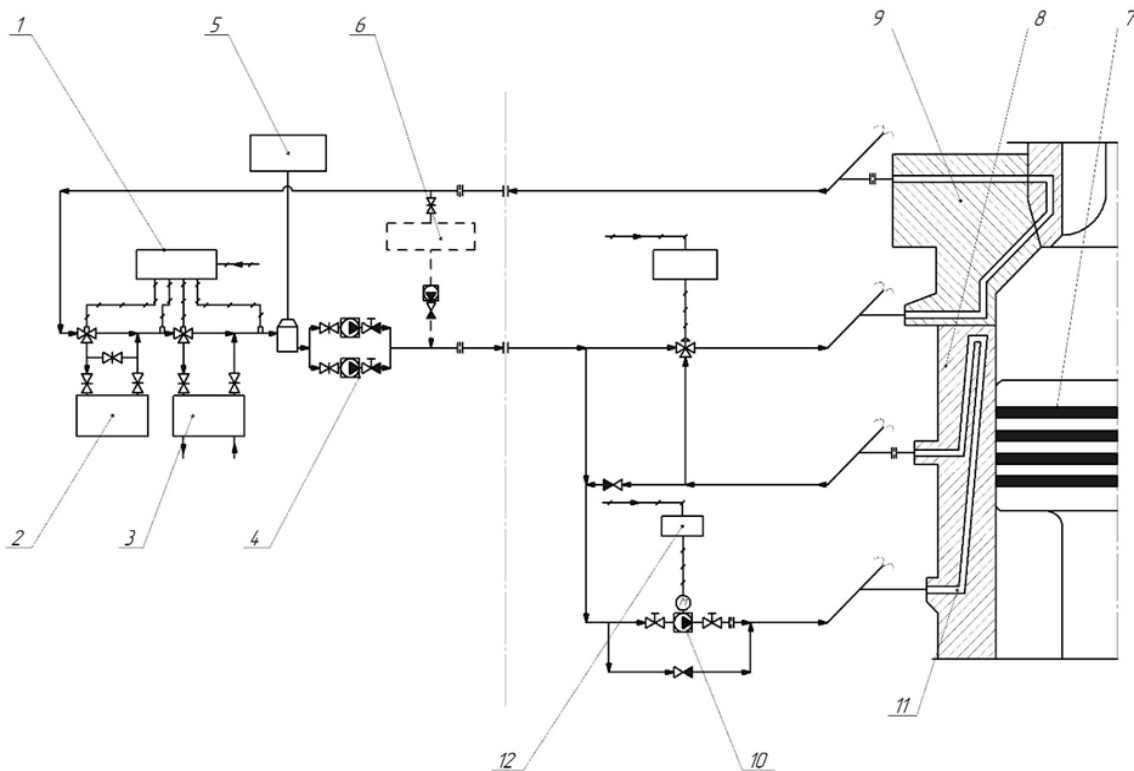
Принципова схема роботи LDCL: 1 – клапанний контролер; 2 – водоопрієнювальна установка; 3 – теплообмінний апарат; 4 – циркуляційний насос системи охолодження; 5 – розширювальний бак; 6 – підігрівач; 7 – поршень; 8 – циліндрова втулка; 9 – циліндрова кришка; 10 – циркуляційний насос системи LDCL; 11 – канал охолодження циліндрової втулки; 12 – перетворювач частоти обертання насосу
